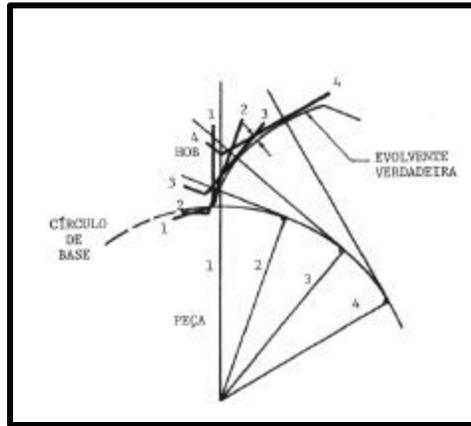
Família de tangentes formadas no corte com ferramenta caracol
